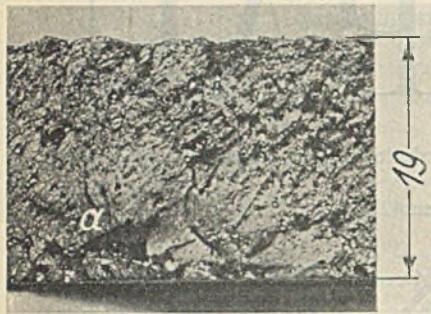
Bruchfläche einer Lichtbogenschweißung. Der Dauerbruch begann bei *a*.
